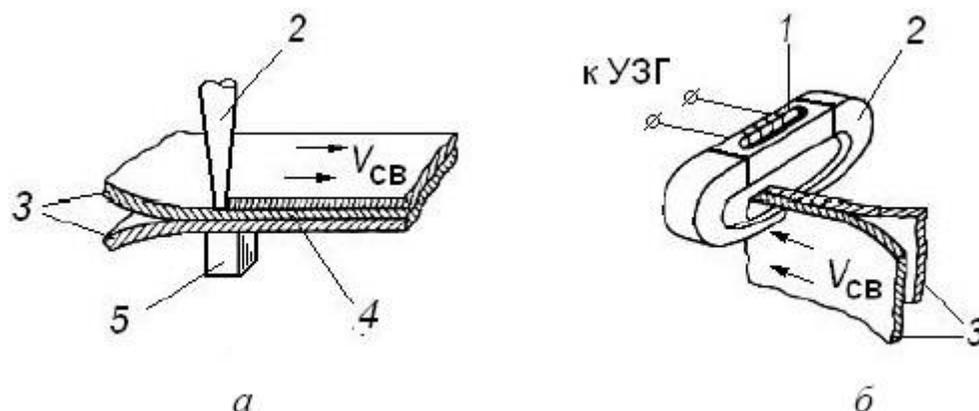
Схема шовной сварки «на протяг» с односторонним (а) и двусторонним (б) подводом УЗ колебаний: 1 – преобразователь; 2 – волновод; 3 – свариваемый материал; 4 – сварной шов; 5 – опора
